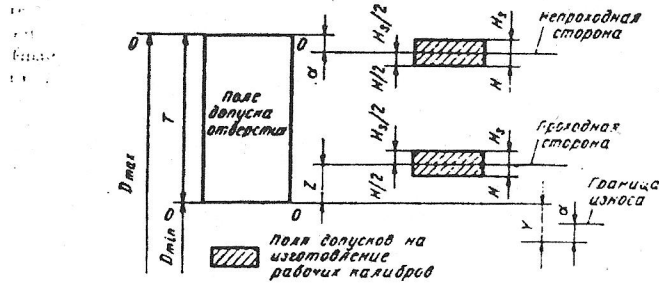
Схема расположения полей допусков калибров для отверстий
